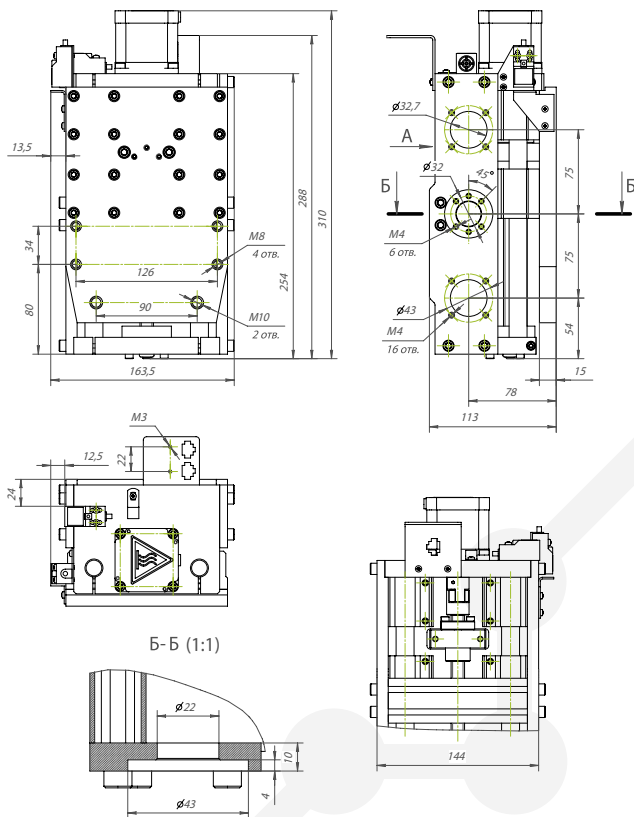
Габаритный чертёж модуля оси Z RY-Z100-RA4
